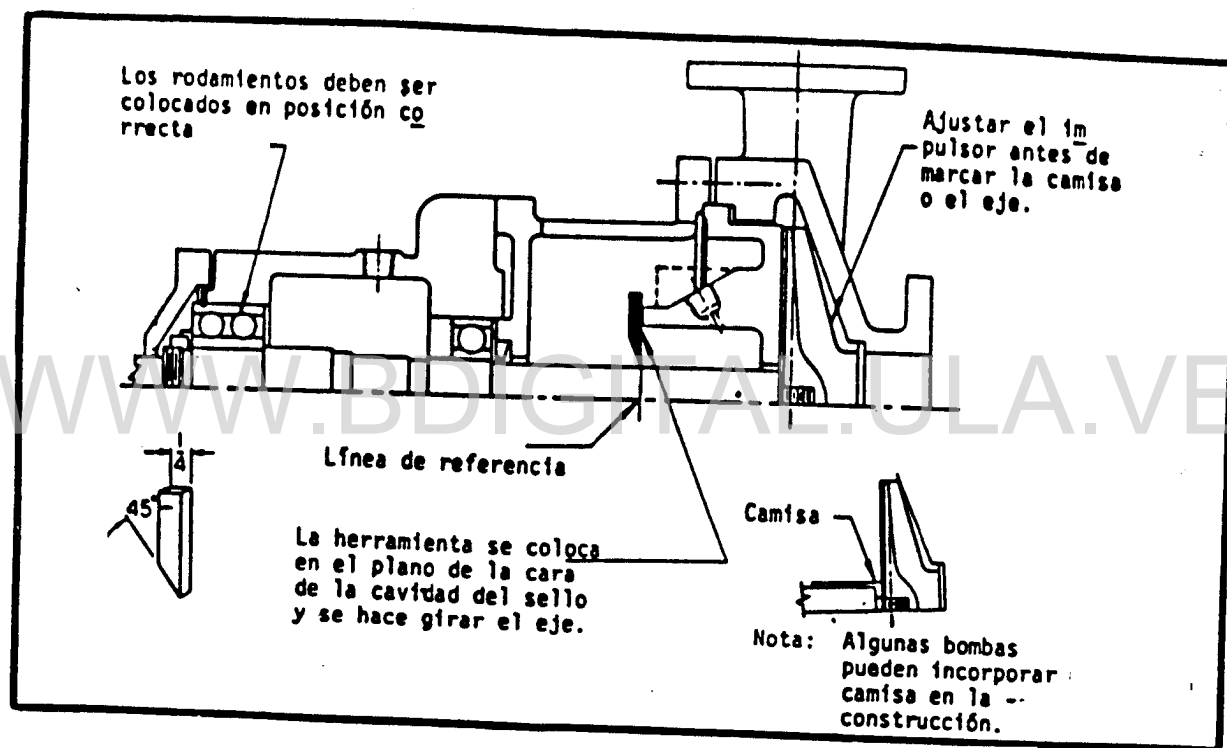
Herramienta utilizada para marcar la línea de referencia
